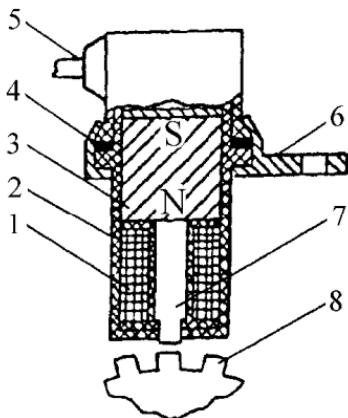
Конструкция датчика положения коленчатого вала:
